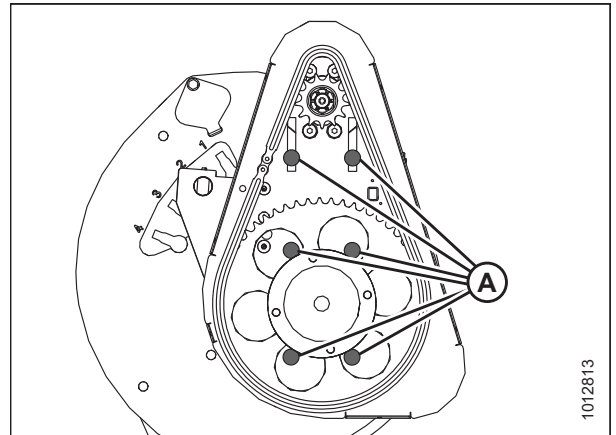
Зображено привод одинарного мотовила — привод подвійного мотовила має таку ж конструкцію
